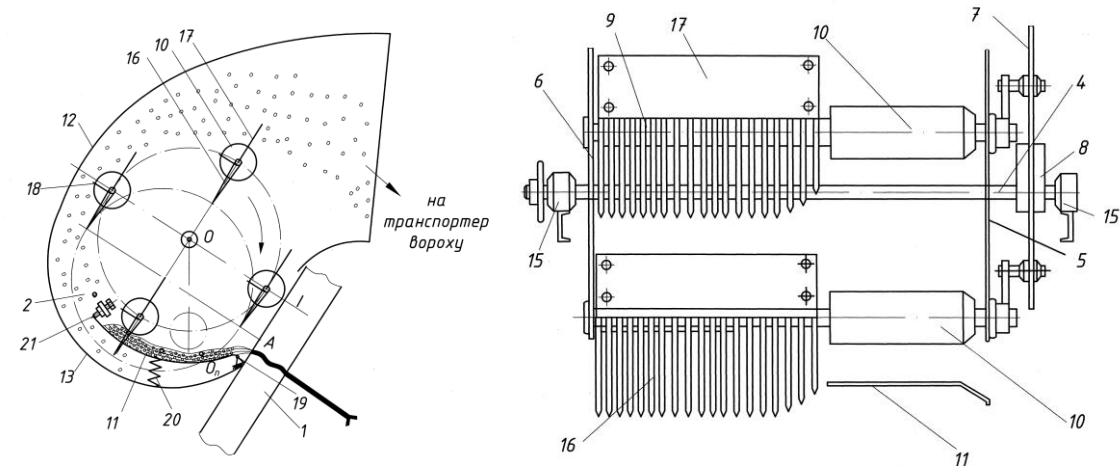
Плющильно-обчисувальний апарат: 1 – затискний транспортер; 2 – обчисувальна камера; 3 – барабан; 4 – вал; 5, 6, 7 – диски; 8 – ексцентриковий механізм; 9 – гребенями; 10 – плющильні вальці; 11 – опорна направляюча поверхня; 12 – корпус; 13 – піддон; 14, 15 – підшипники; 16 – обчисувальні зуби; 17, 18 – лопаті; 19 – куліса; 20 – пружина; 21 – упор.
